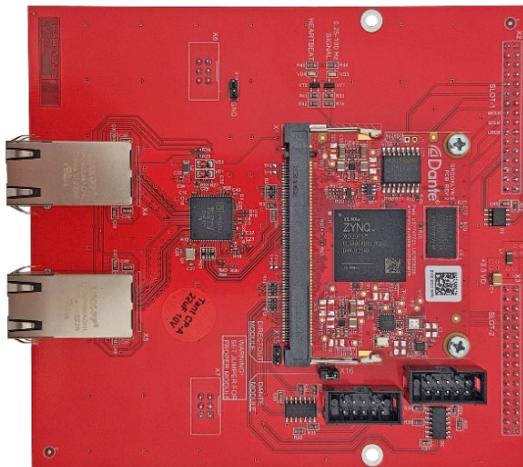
Внешний вид модуля TP-804- Dante
